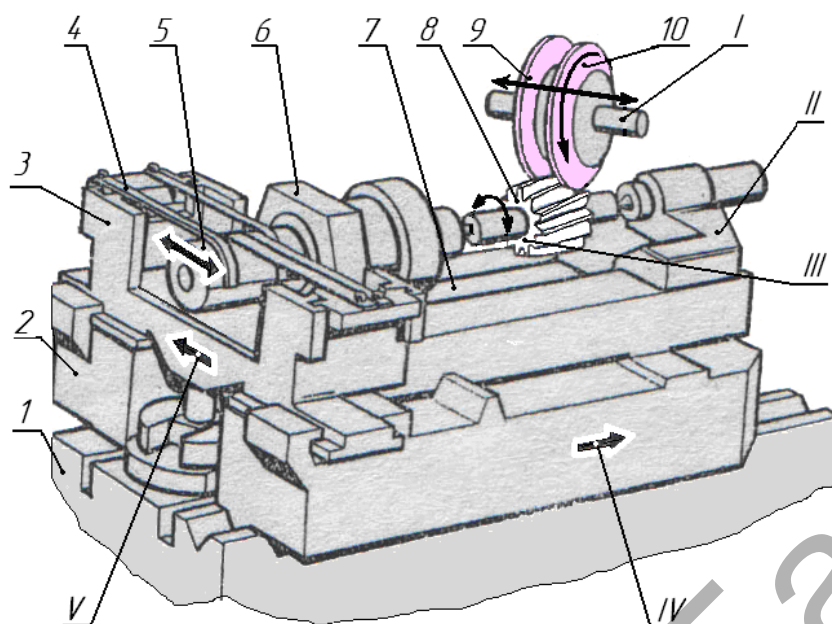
Схема шлифования зубчатых колес тарельчатыми кругами и схемы их установки
